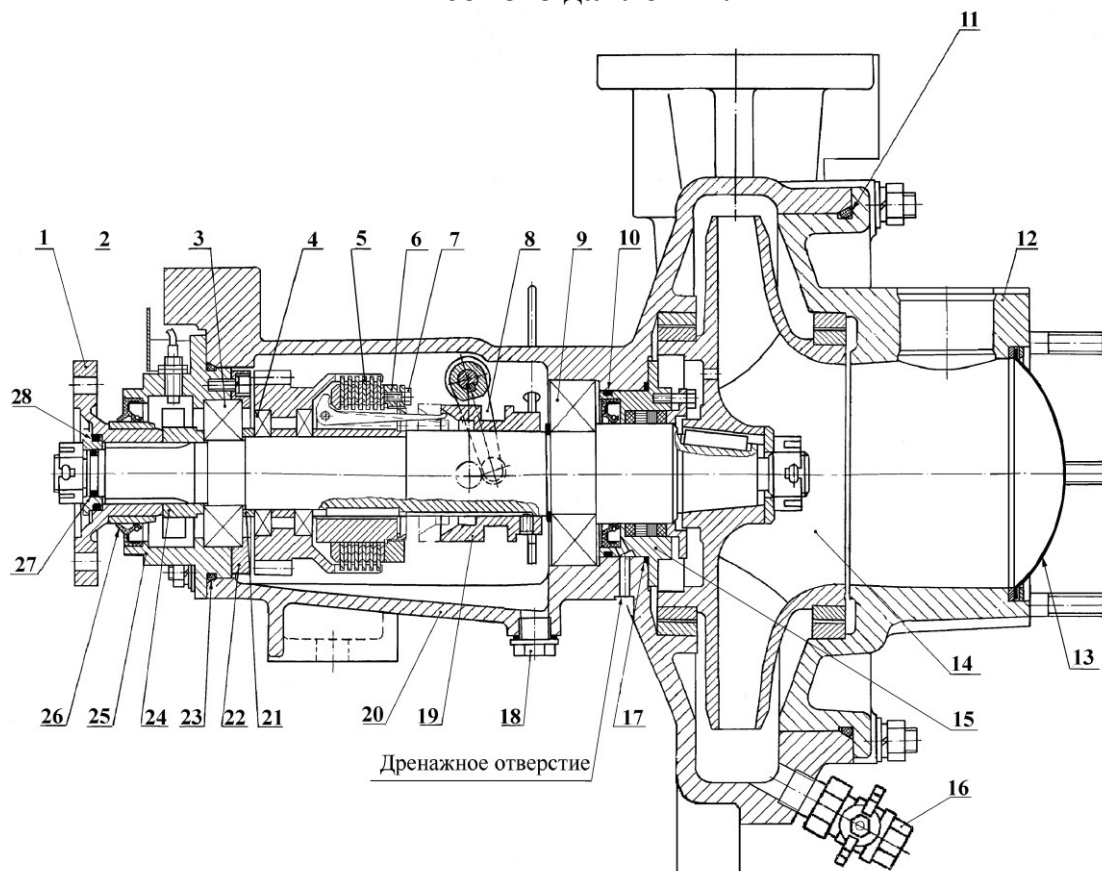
Ступень нормального давления: 1 - -полумуфта; 2 - датчик тахометра; 3 - подшипник; 4 - подшипник; 5 - муфта фрикционная; 6 - гайка регулировочная; 7 - болт стопорный; 8 - вилка; 9 - подшипник; 12 - крышка насоса; 13 - сетка; 14 - колесо рабочее; 15 - сальниковое уплотнение вала; 16 - кран сливной; 18 - пробка сливная; 19 - втулка нажимная; 20 - корпус насоса; 21 - кольцо; 22 - накладка; 24 - ротор; 25 - корпус задней опоры; 26 – манжета; 10, 11, 17, 23, 27, 28 -- кольца уплотнительные.
